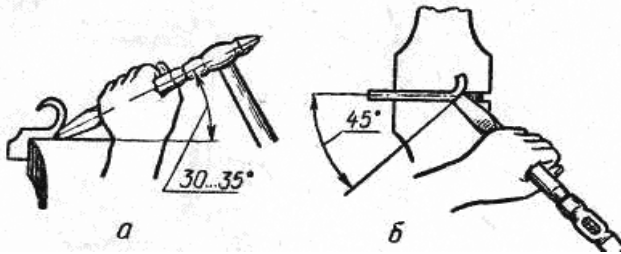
Рубання листового металу в лещатах: а, б – нахил зубила відповідно до оброблюваної поверхні та осі губок
